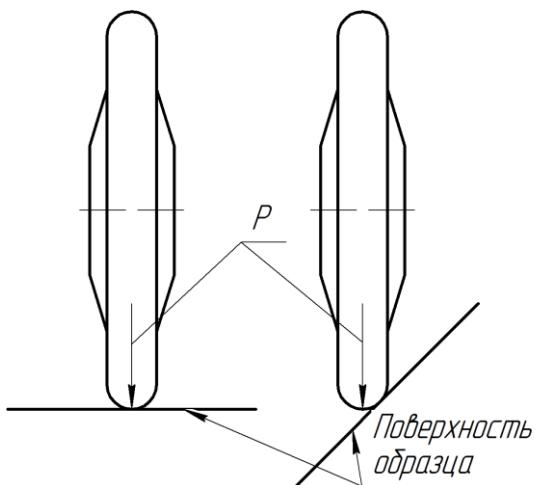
Сравнение схем обкатывания по упругой схеме цилиндрической и наклонной поверхностей
